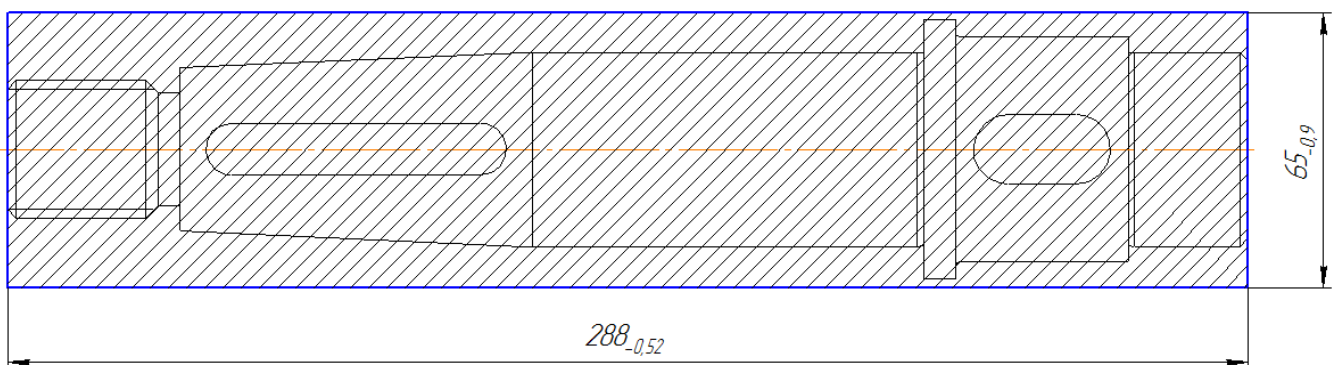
Ескіз заготовки - прокат розрізаний пилою
